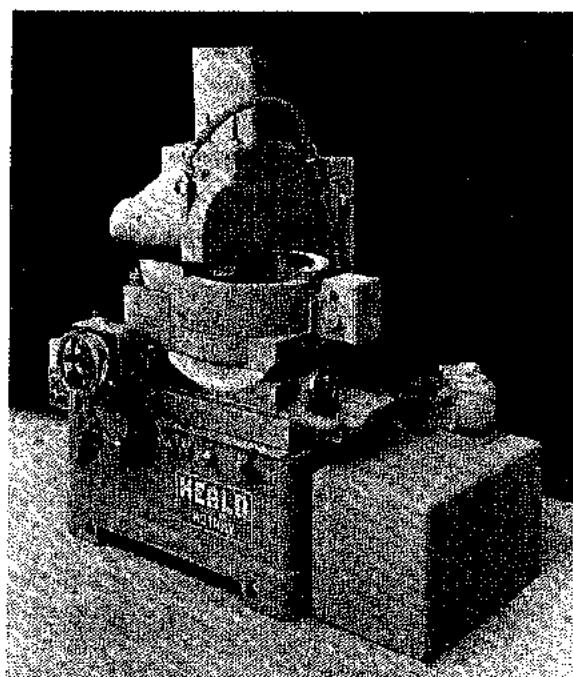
Rectificadora de mesa giratoria y husillo horizontal (Heald Machine Co.).
